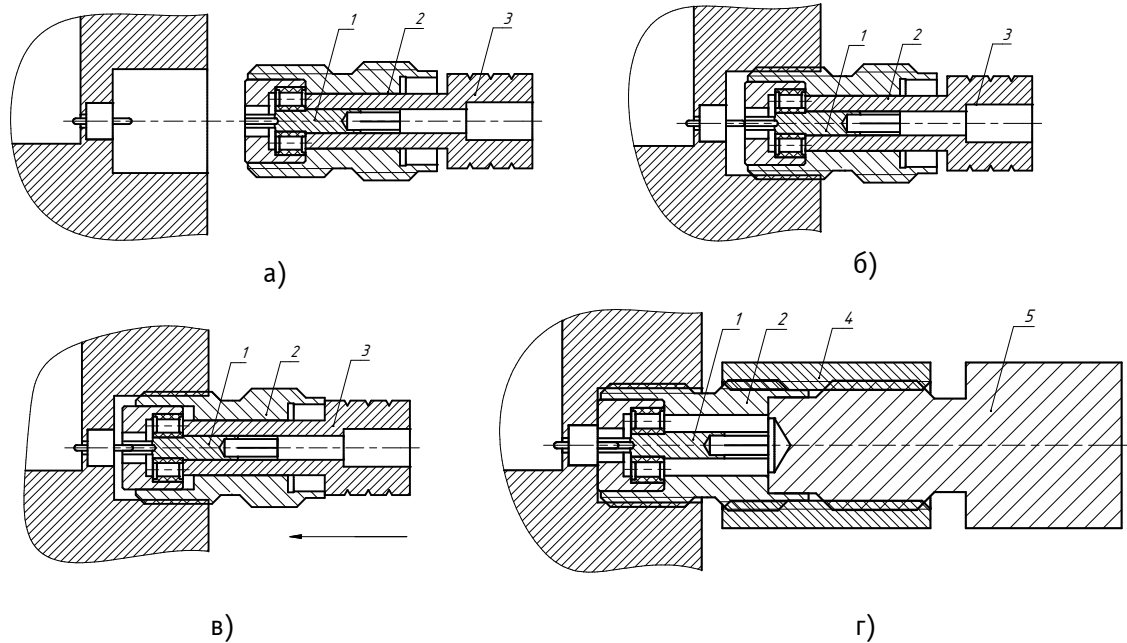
Общий принцип монтажа блочных резьбовых соединителей типа розетка
